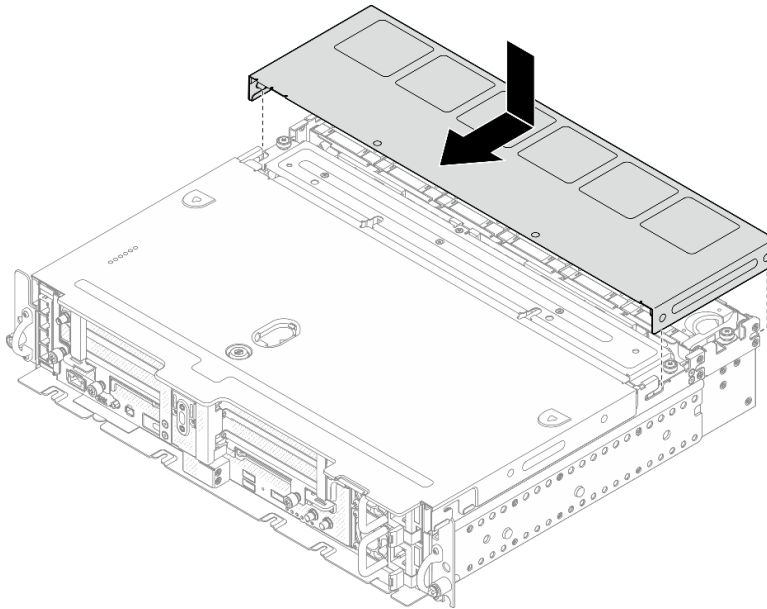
Instalación de la cubierta del ventilador (360 mm)
